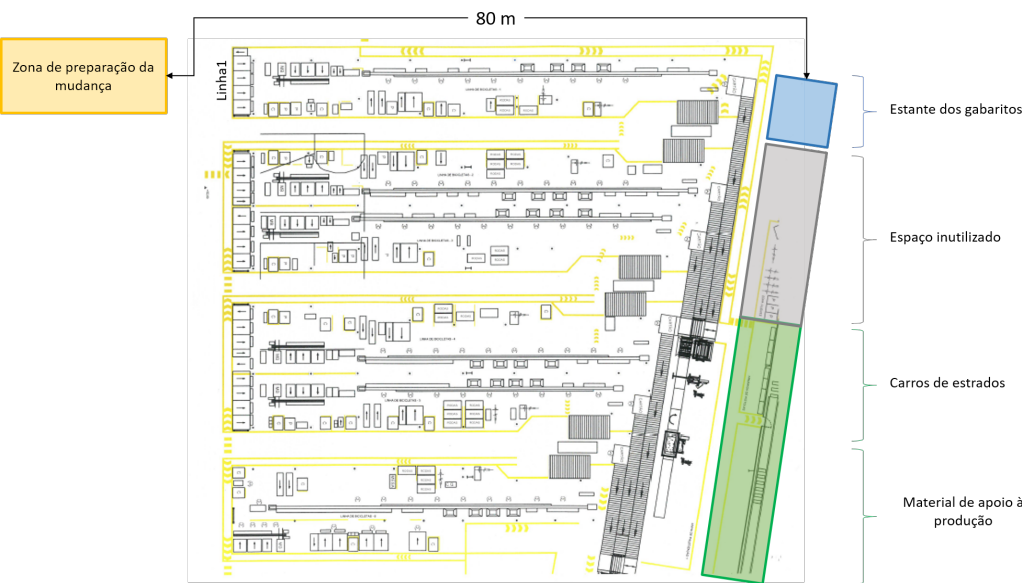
Planta da RTE com zonas iniciais de arrumação das ferramentas e materiais
